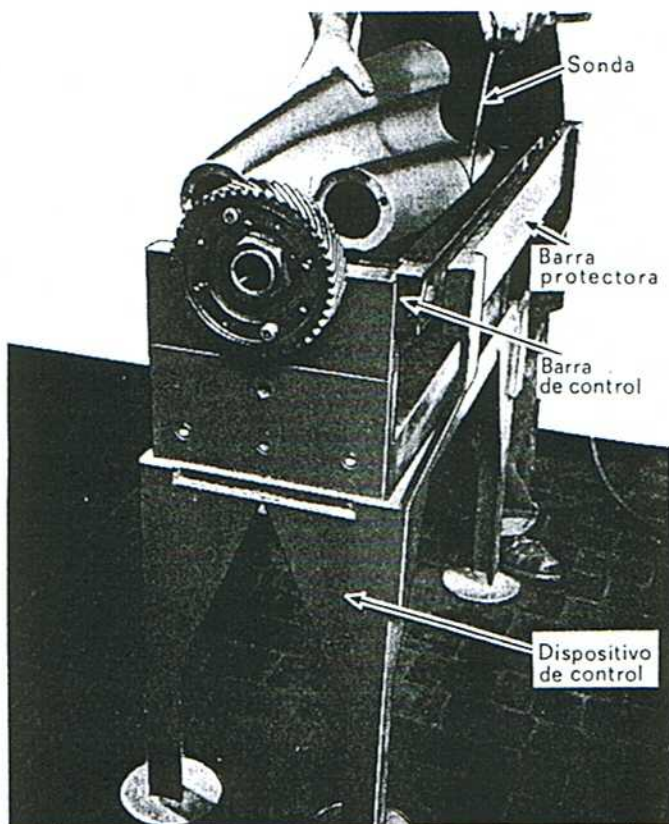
Forma de comprobar la holgura entre rotor y carcasa empleando el dispositivo de comprobación 8268442.
